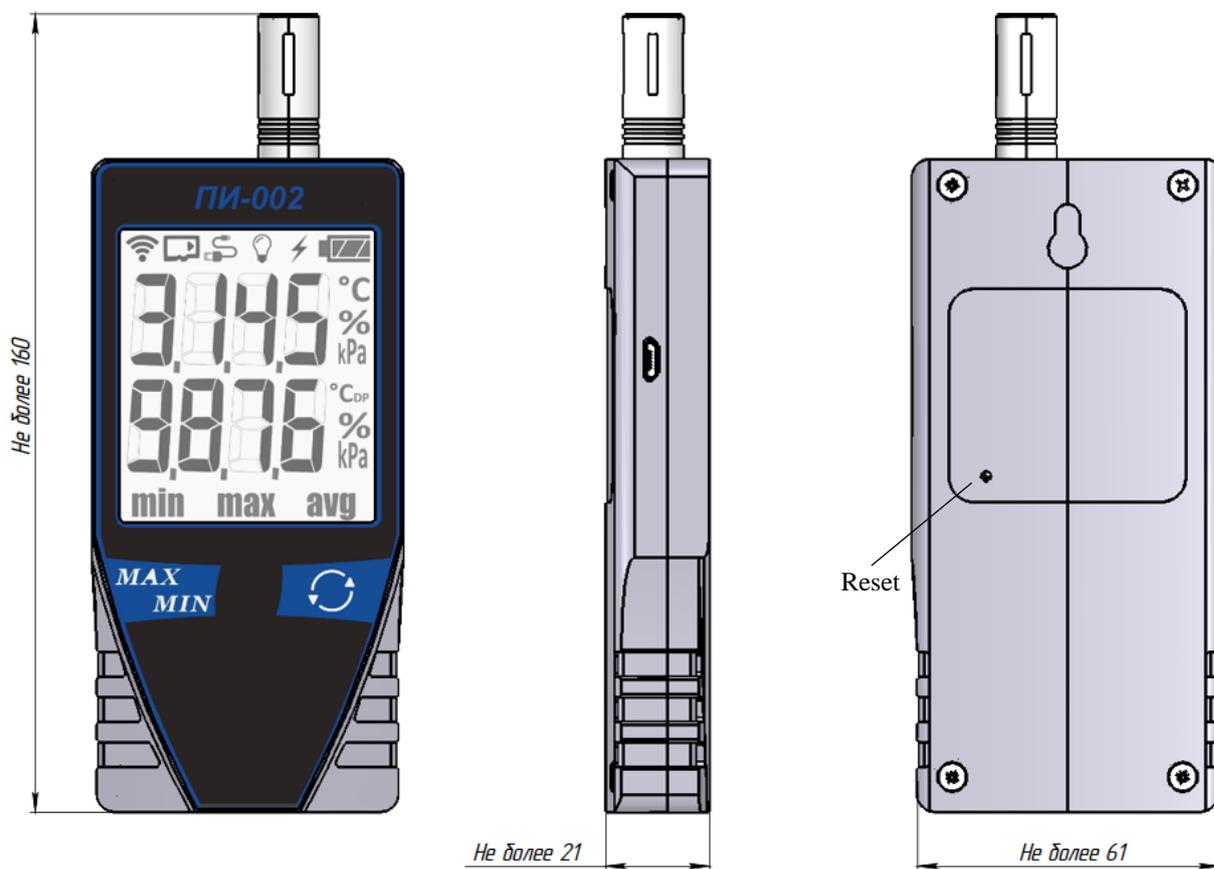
габаритные размеры ПИ-002/1М.Д
